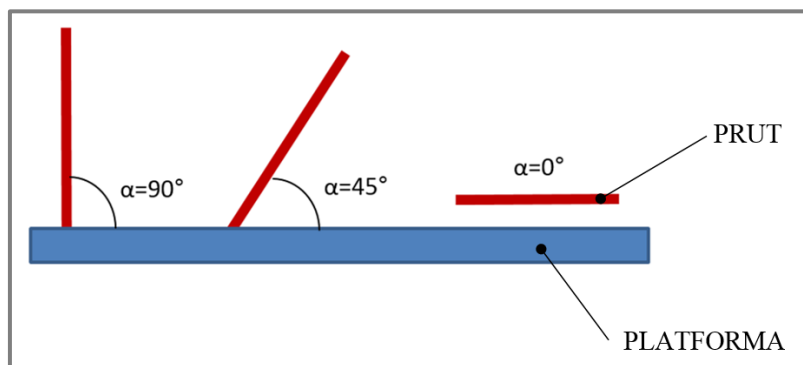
Vizualizace modelu testovacího tělesa s pruty
